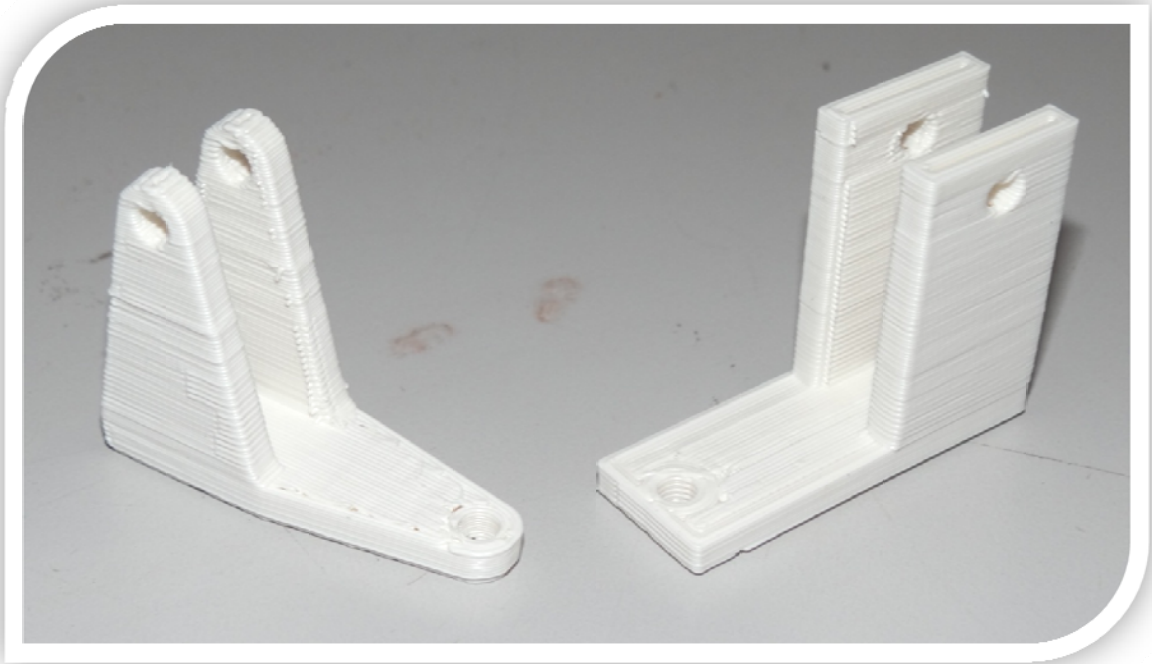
Imagen del primer diseño de bastidor (derecha) y del segundo diseño (izquierda). [Fuente: Elaboración propia.]
